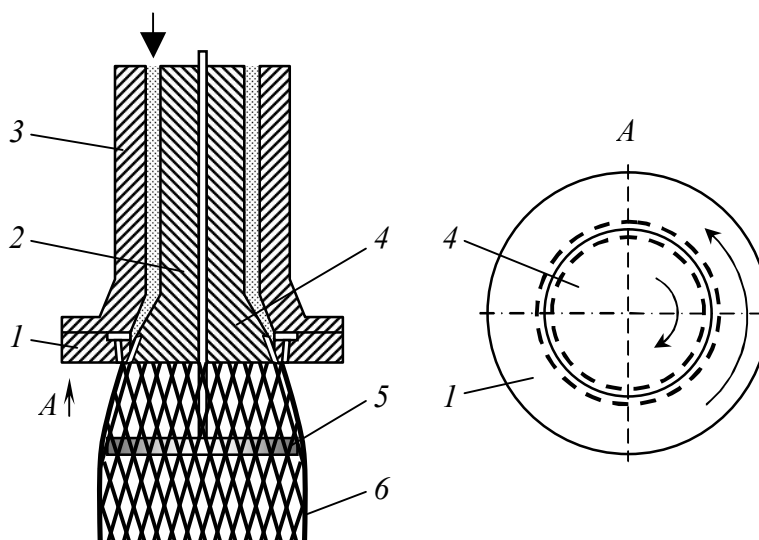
Способ получения рукавных полимерных сеток экструзией расплава через продольные отверстия вращающихся фильер: 1 – внешняя фильера; 2 – вал; 3 – корпус; 4 – внутренняя фильера; 5 – ширительный диск; 6 – готовая сетка
